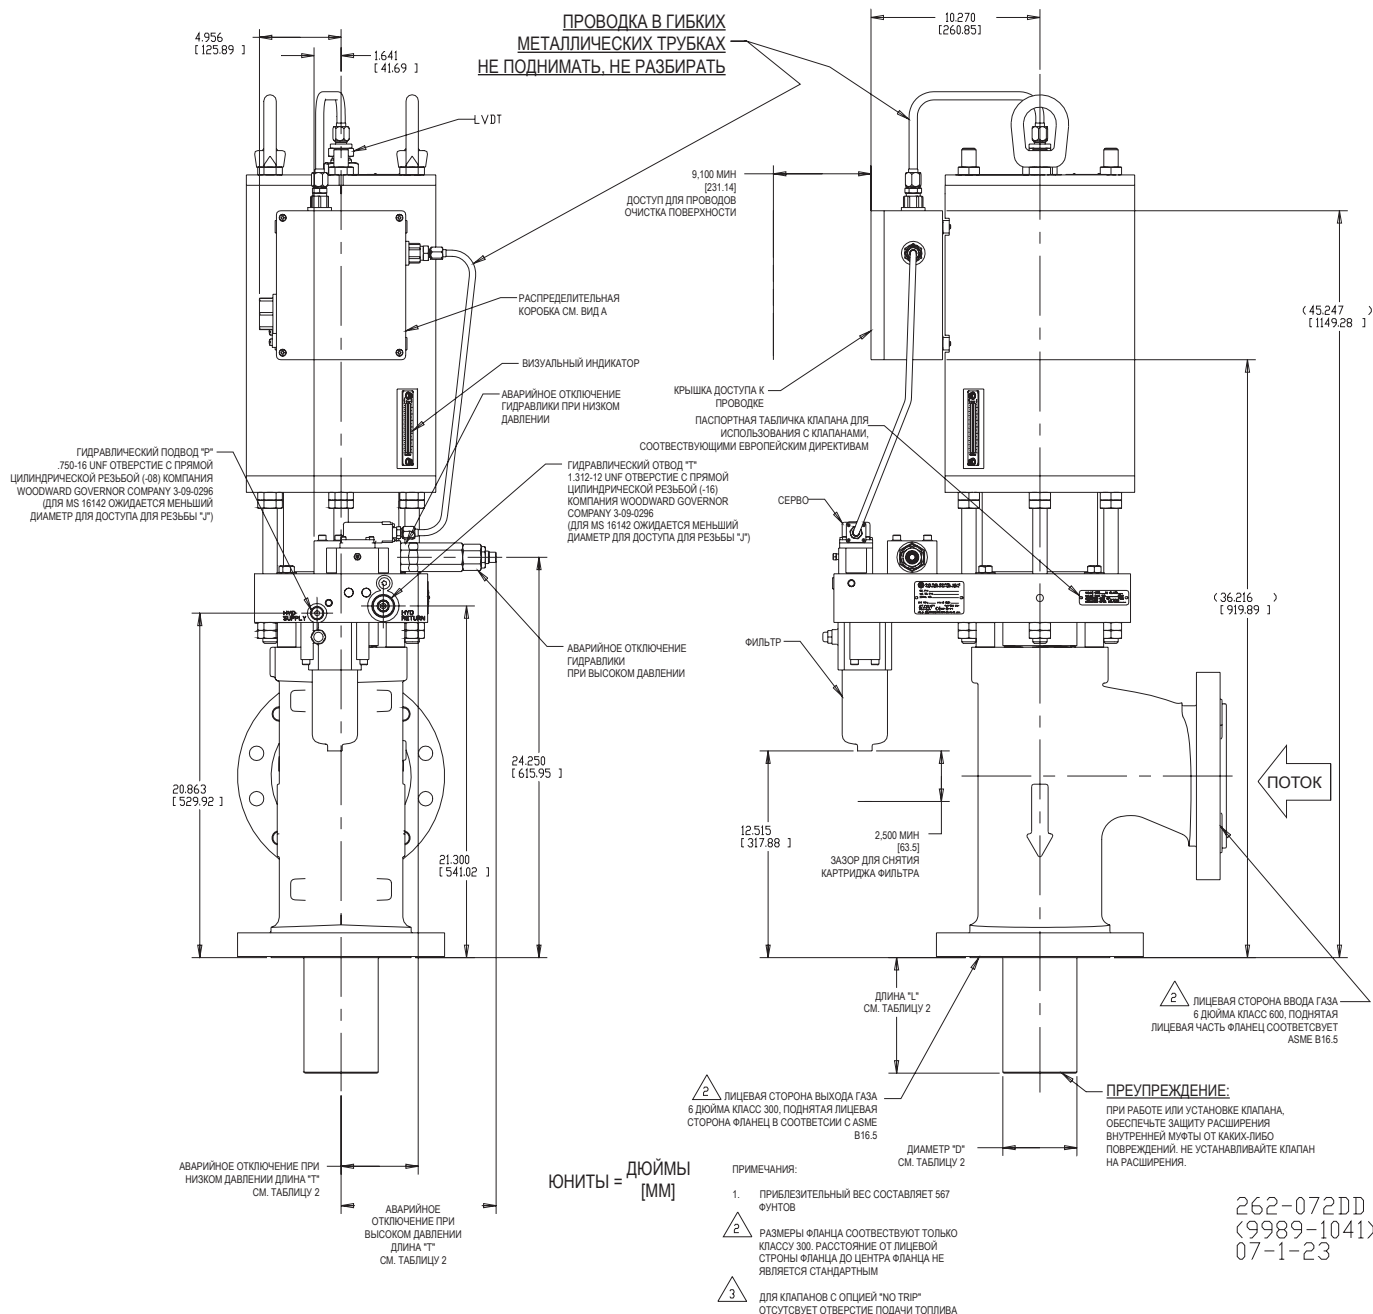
Габаритный чертеж клапана SonicFlo (6-дюймовый, класс 300)
